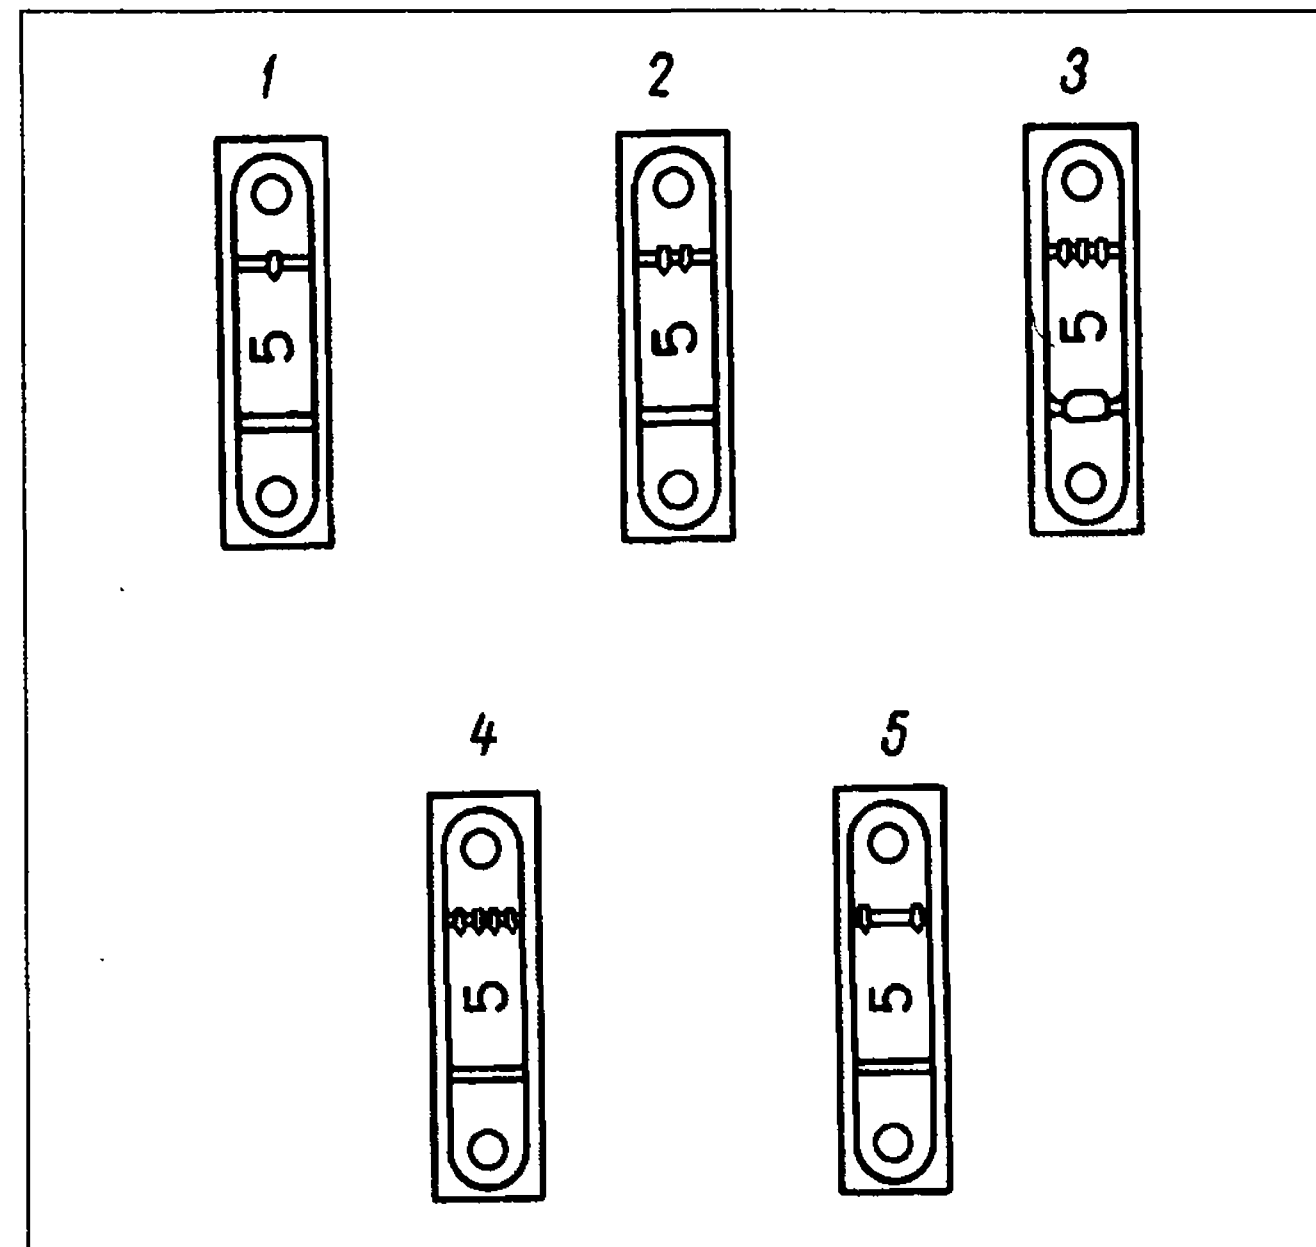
Метки на крышках коренных подшипников (счет опор ведется от передней части двигателя) и условный номер блока цилиндров
